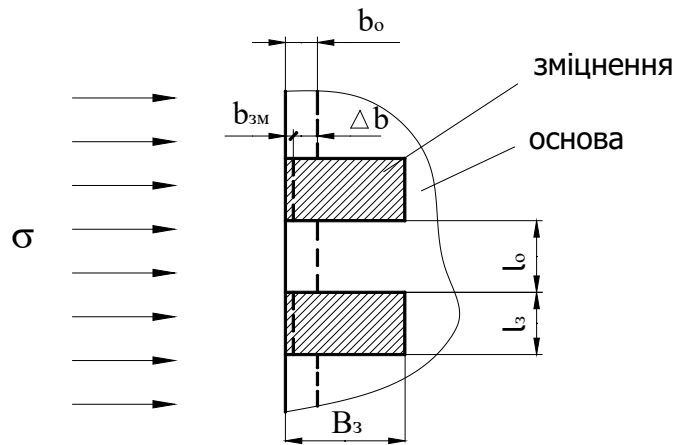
Схема зношування ріжучої кромки наральника з локальними ділянками зміцнення
